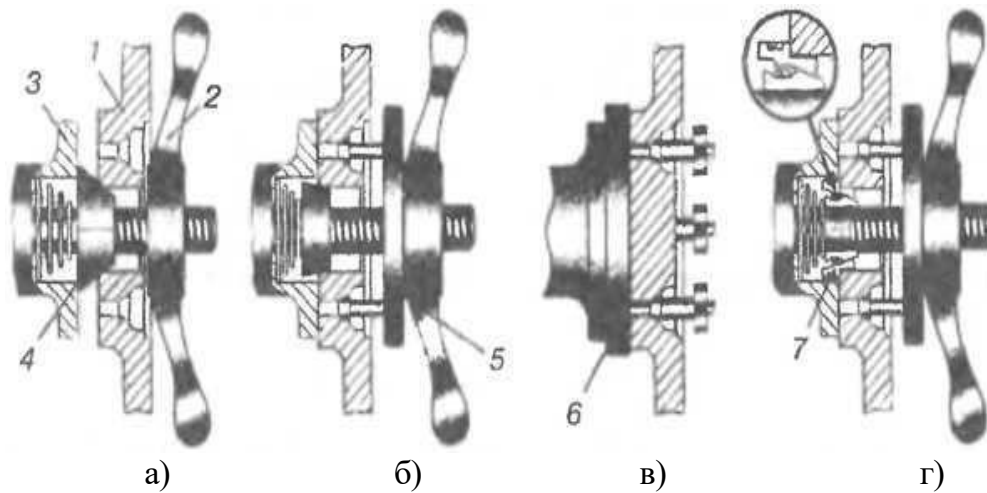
Способи і пристрої центрування колеса на валу балансувального верстату.
